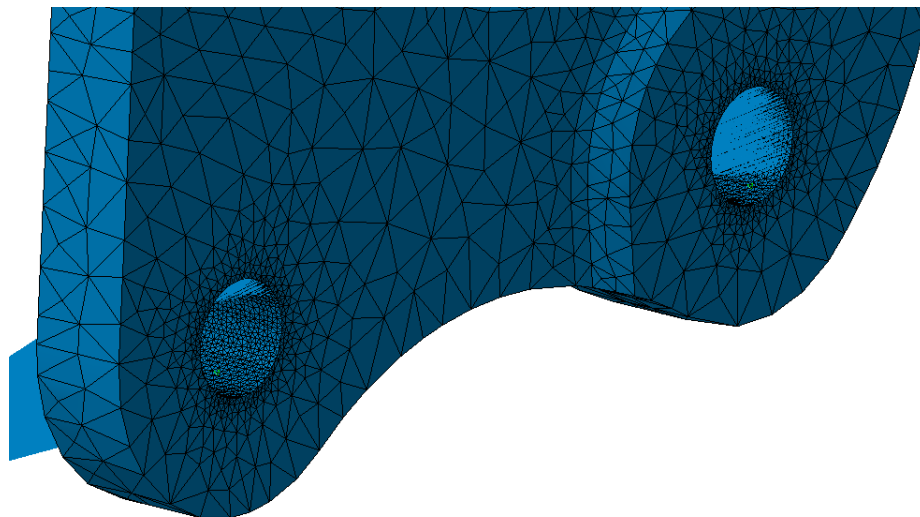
Detalle del refinado en los anclajes de la horquilla de dirección.
